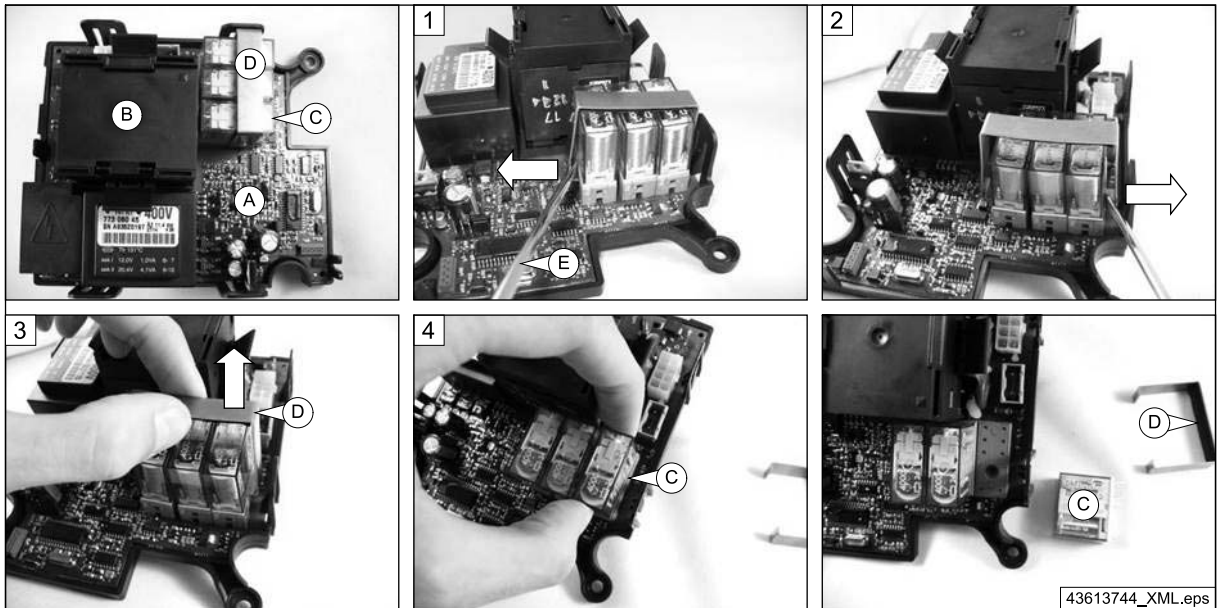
(A) Steuerkarte; (B) Schütz; (C) Relais; (D) Federklammer; (E) Schraubendreher
